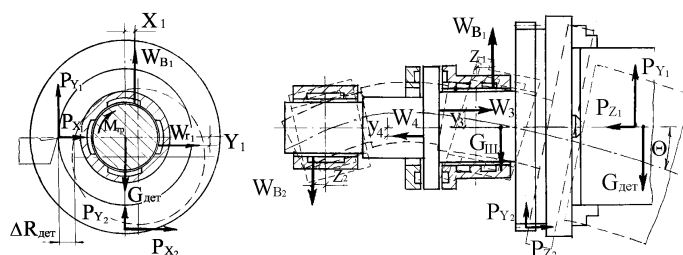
Розрахункова схема шпиндельного вузла важкого токарного верстата
